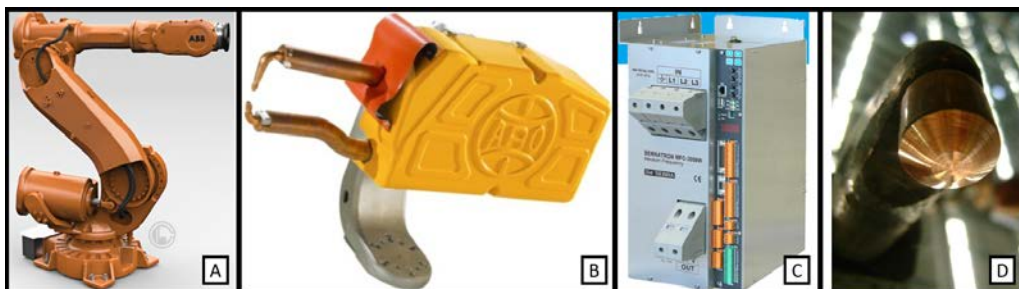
(a) Robô ABB IRB 6640; (b) Pinça de Solda ARO 3G R3X; (c) Controlador de solda SERRA MFC 3007W; (d) Ponteira do eletrodo após fresagem.
